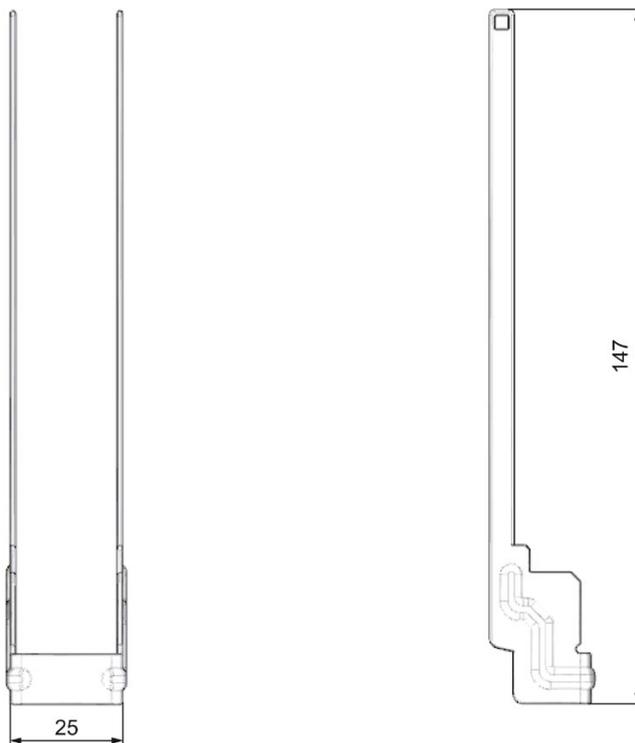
Croquis acotado del estribo de pantalla para módulos de 35 mm
